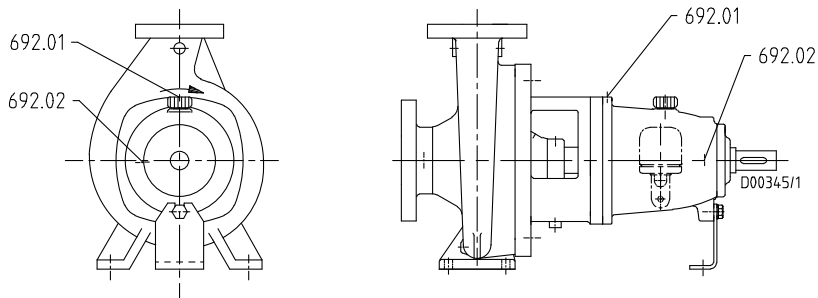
Присоединения СРКН, НРК: корпус подшипника UP02/ P02as
